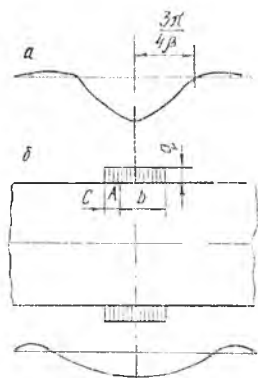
Перемещение оболочки при сварке кольцевого шва без приспособления (а) и с разжимным кольцом (б)
